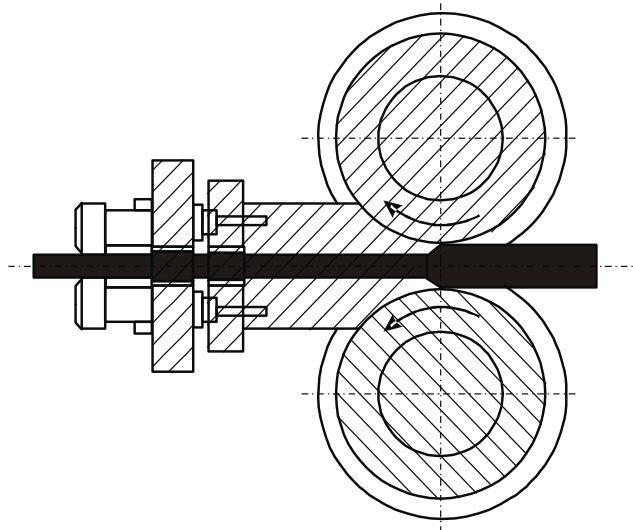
Схема пристрою для процесу Електролінг: 1- робочі валки; 2 – матриця; 3 – заготовка; 4 - виріб
